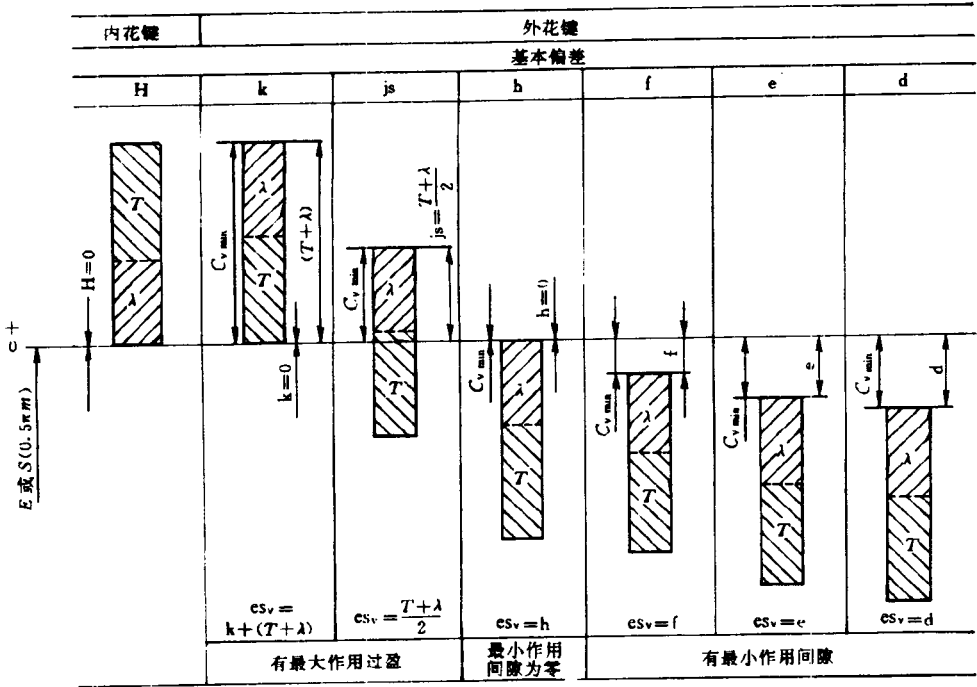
渐开线花键的配合尺寸公差带和六类配合
